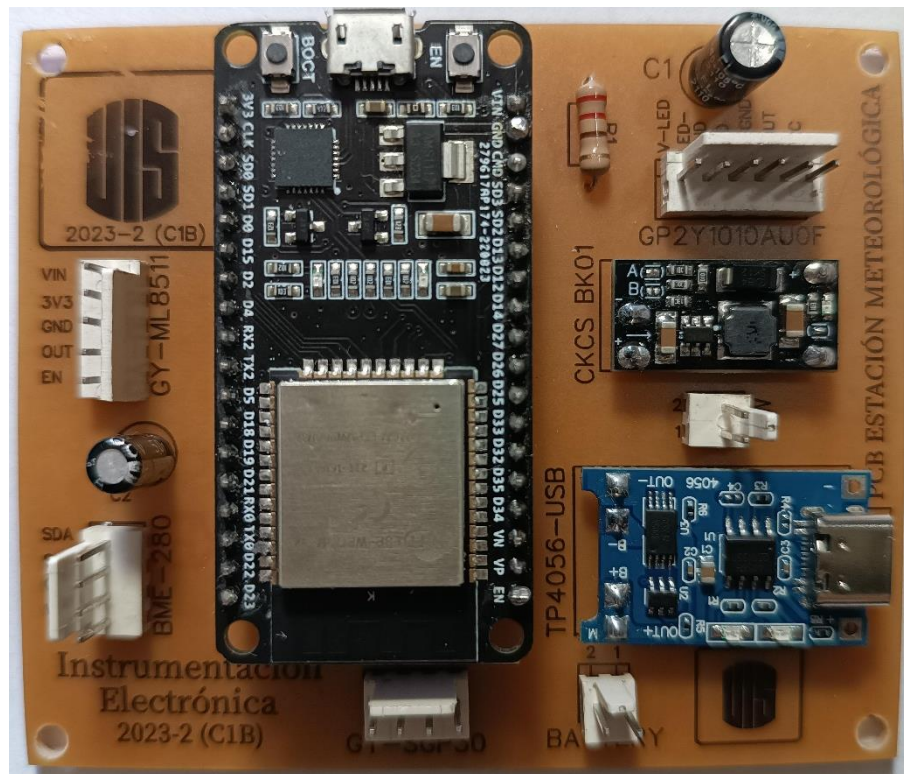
Segundo rediseño PCB C1B v2.1 (Superior)
